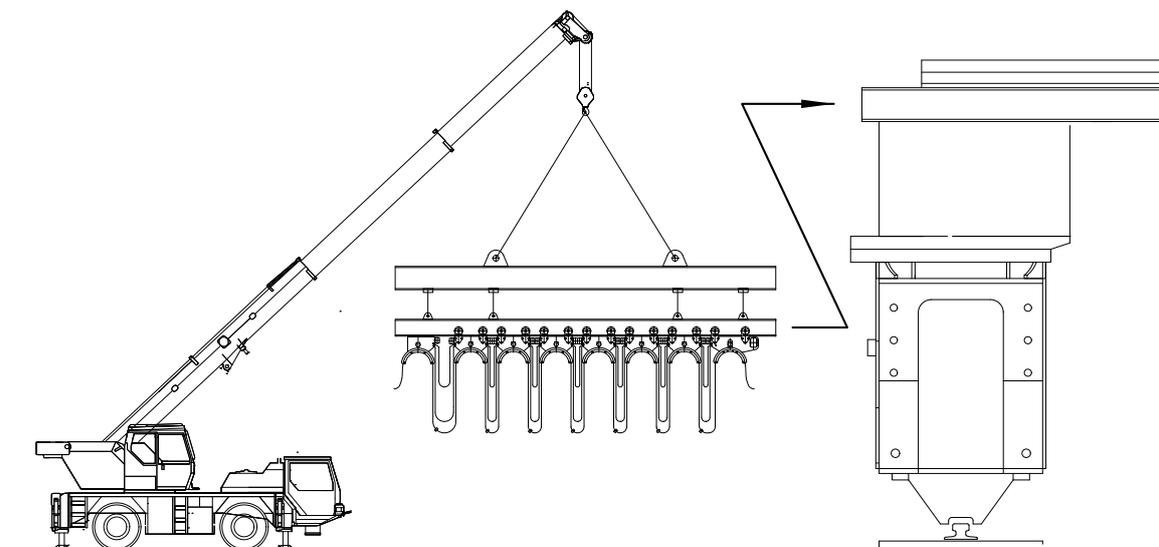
Montaggio di un sistema di carrelli portacavi premontato
